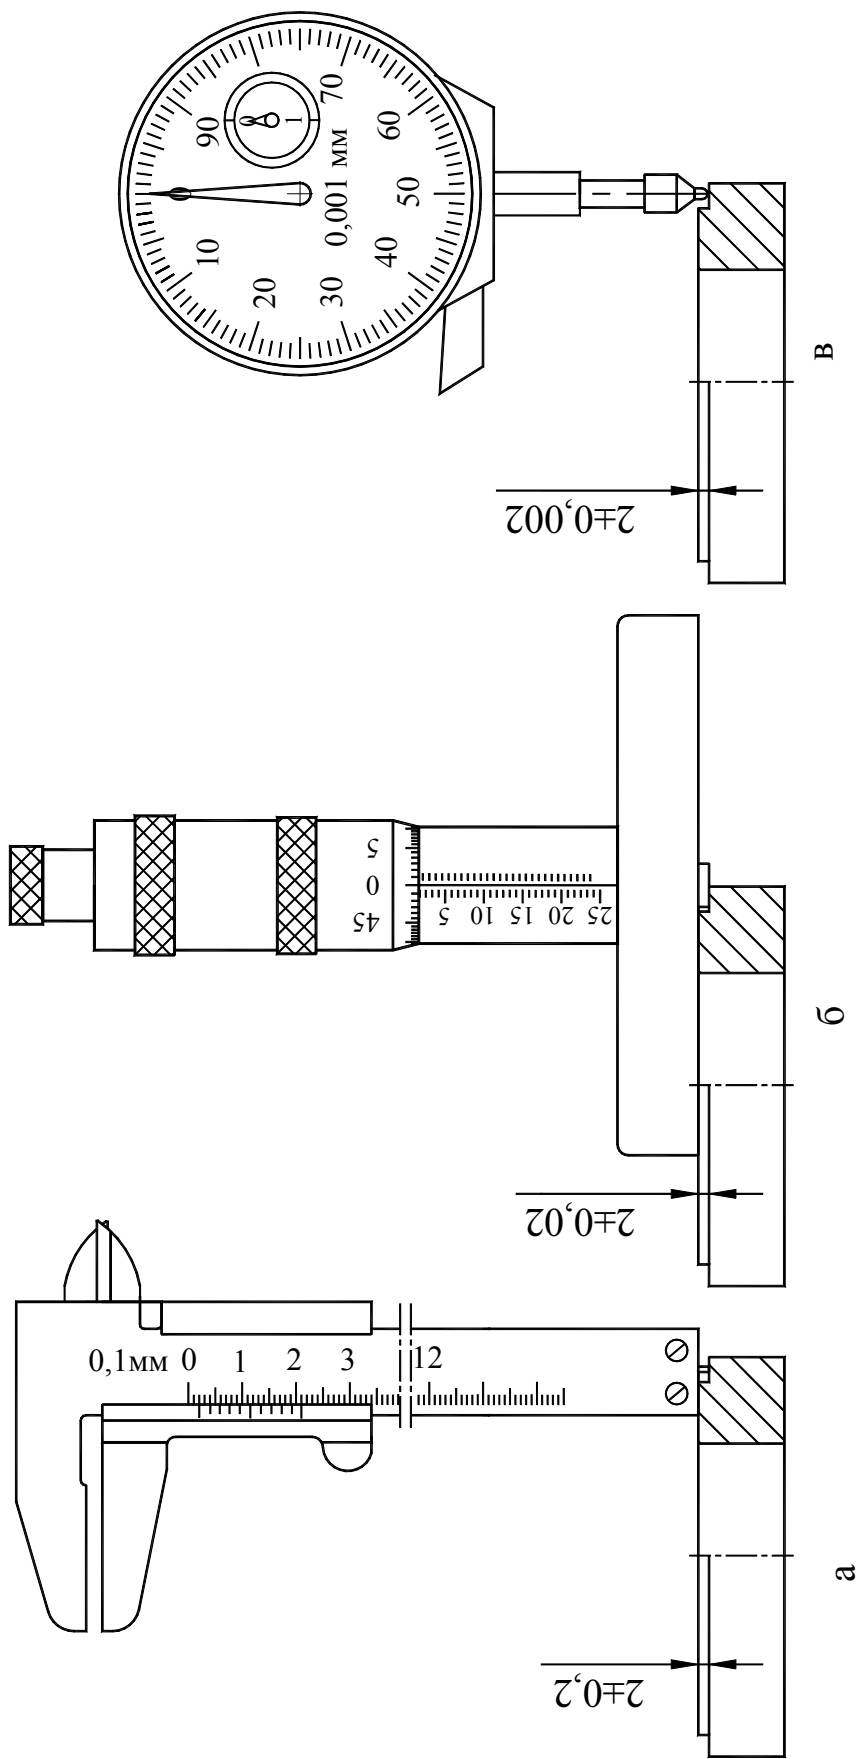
Схемы измерения линейного размера 2 мм с различными по точности допусками:
